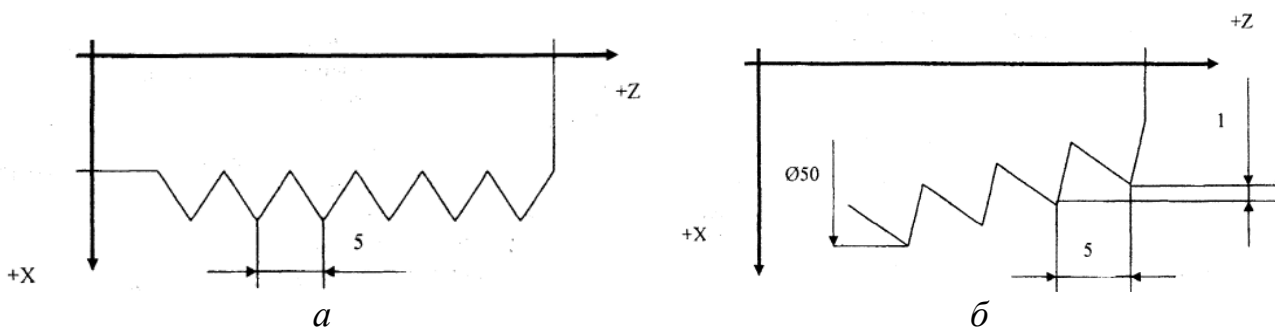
Нарезание резьбы: а - цилиндрическая резьба; б - коническая резьба
